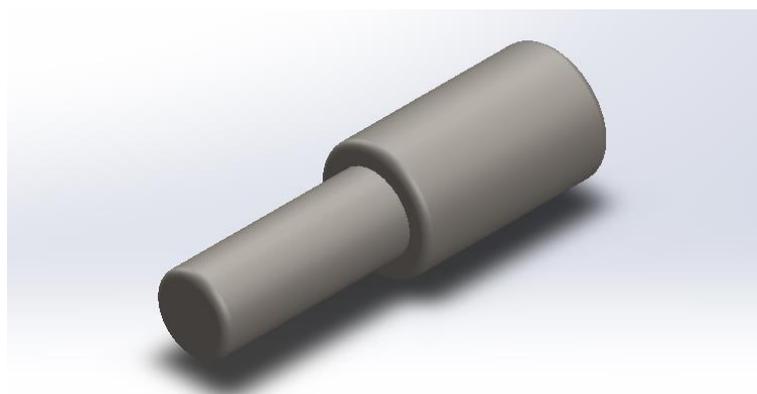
Vista isométrica del fusible mecánico. Fuente: Captura SolidWorks
